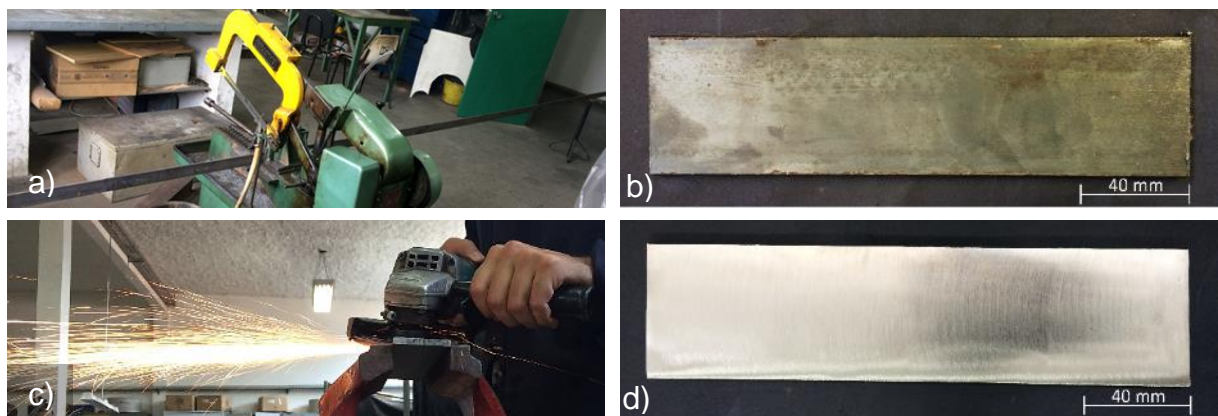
Preparação da chapa: a) corte da vara de 6 m de comprimento na serra franho; b) chapa após o corte com 200 mm de comprimento; c) remoção de rebarbas e limpeza da chapa com o flap disco; d) chapa pronta para a soldagem.
